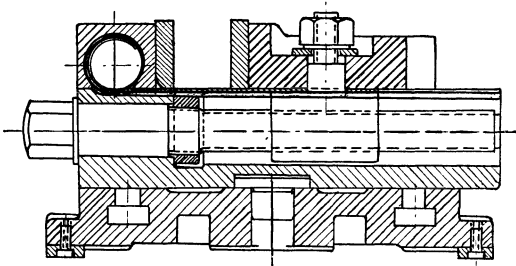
Maschinenschraubstock mit drehbarer Backe, Schnitt.
